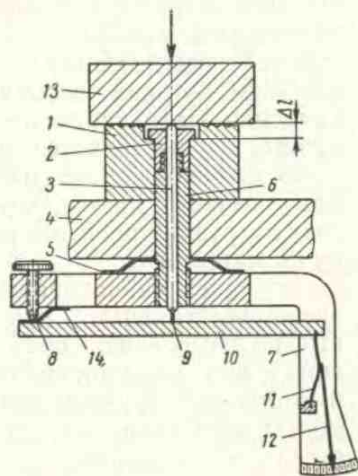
Схема прибора конструкции Н. Б. Демкина для измерения сближения при неподвижном контакте
